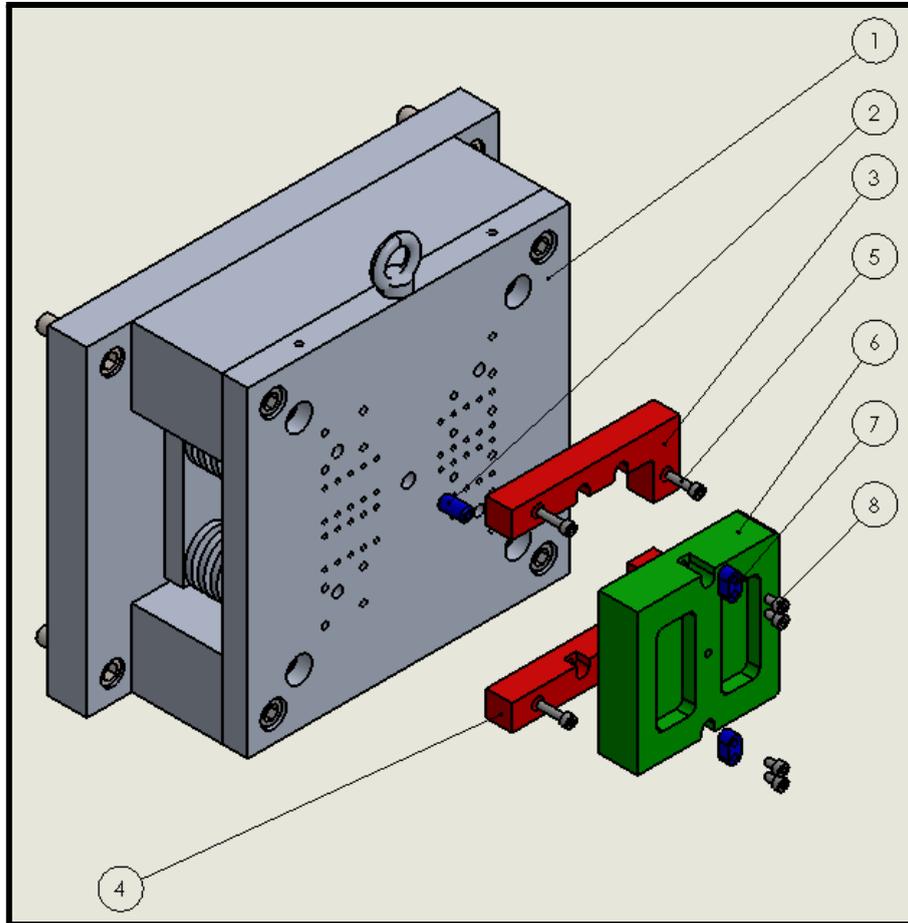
M. Vista explosionada de la configuración 2 del portamolde
